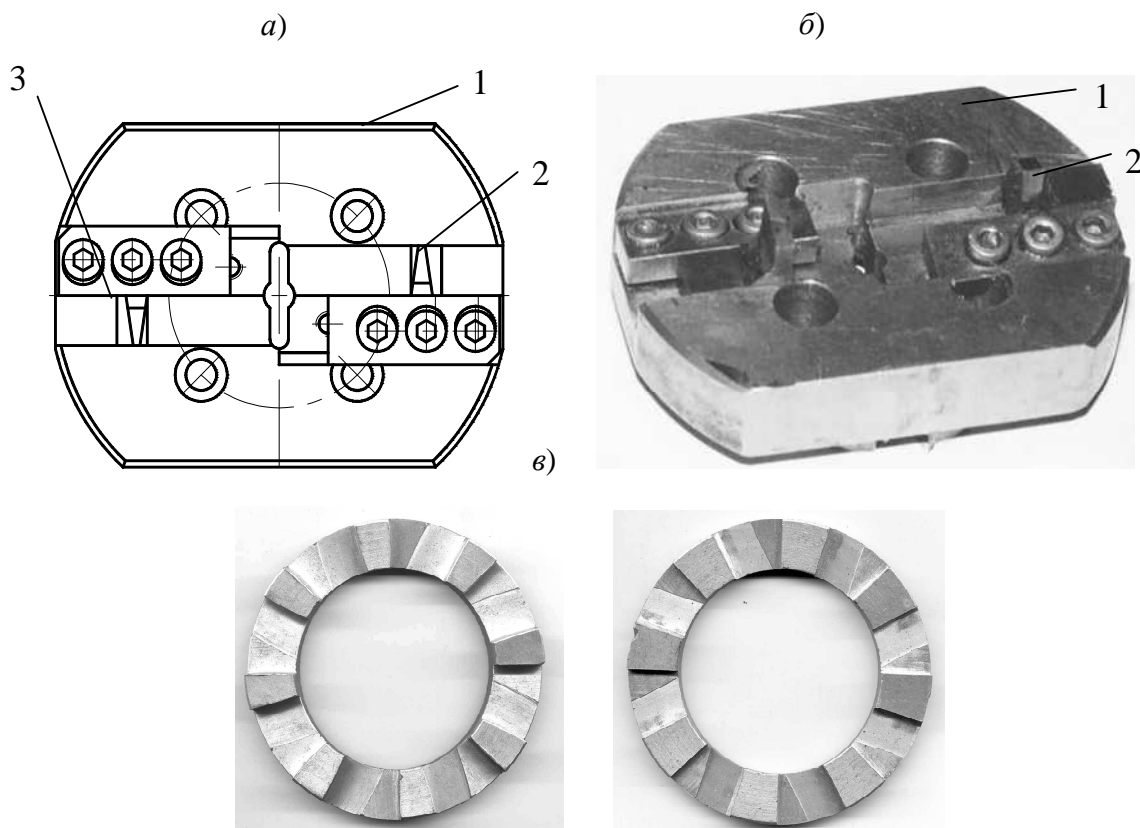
Инструмент к станку модели ВС-50 для обработки сходящихся и расходящихся пазов: а, б – конструкция инструмента; в – обработанные детали с выпуклыми и вогнутыми боковыми сторонами пазов
